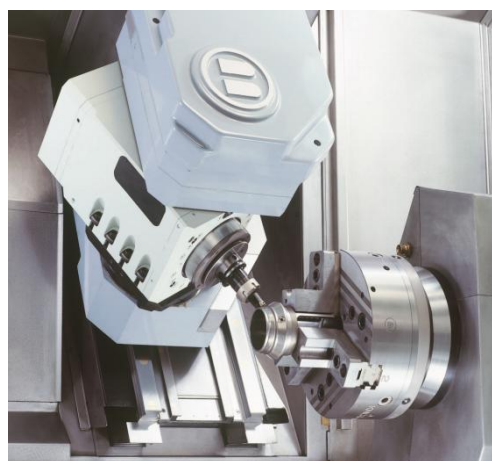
Kinematika obrábění na 5osém soustružnickém obráběcím centru (XYZCB) [8]
